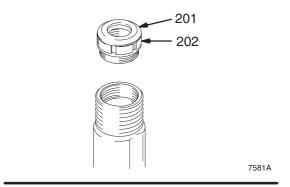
Engrase las empaquetaduras del pistón y el extremo superior del prolongador.
